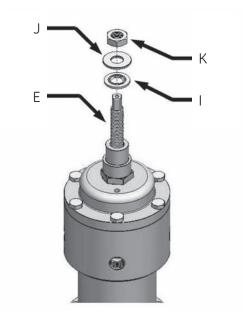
Assemblaggio tenuta filettatura 175/600-CH
